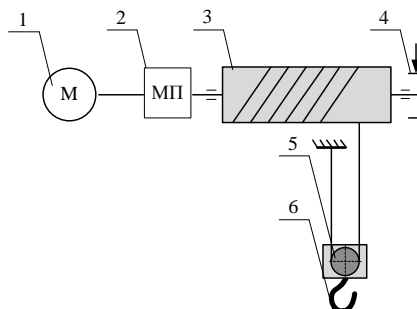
Спрощена кінематична схема барабанної лебідки: 1 – двигун; 2 – механічна передача; 3 – барабан; 4 – гальмівний шків; 5 – поліспаст; 6 – вантажозахватний пристрій
